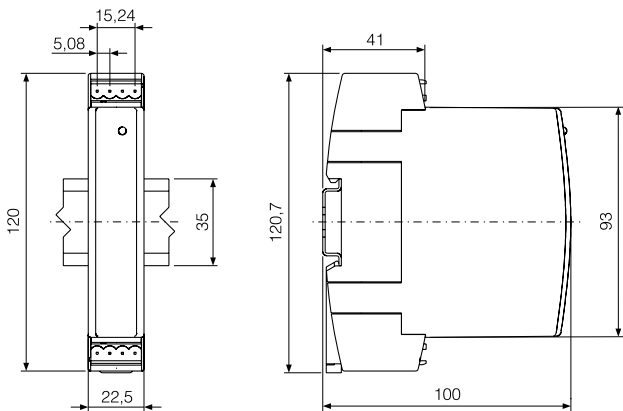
Abmessungen und Montage des Messumformers P20Z
